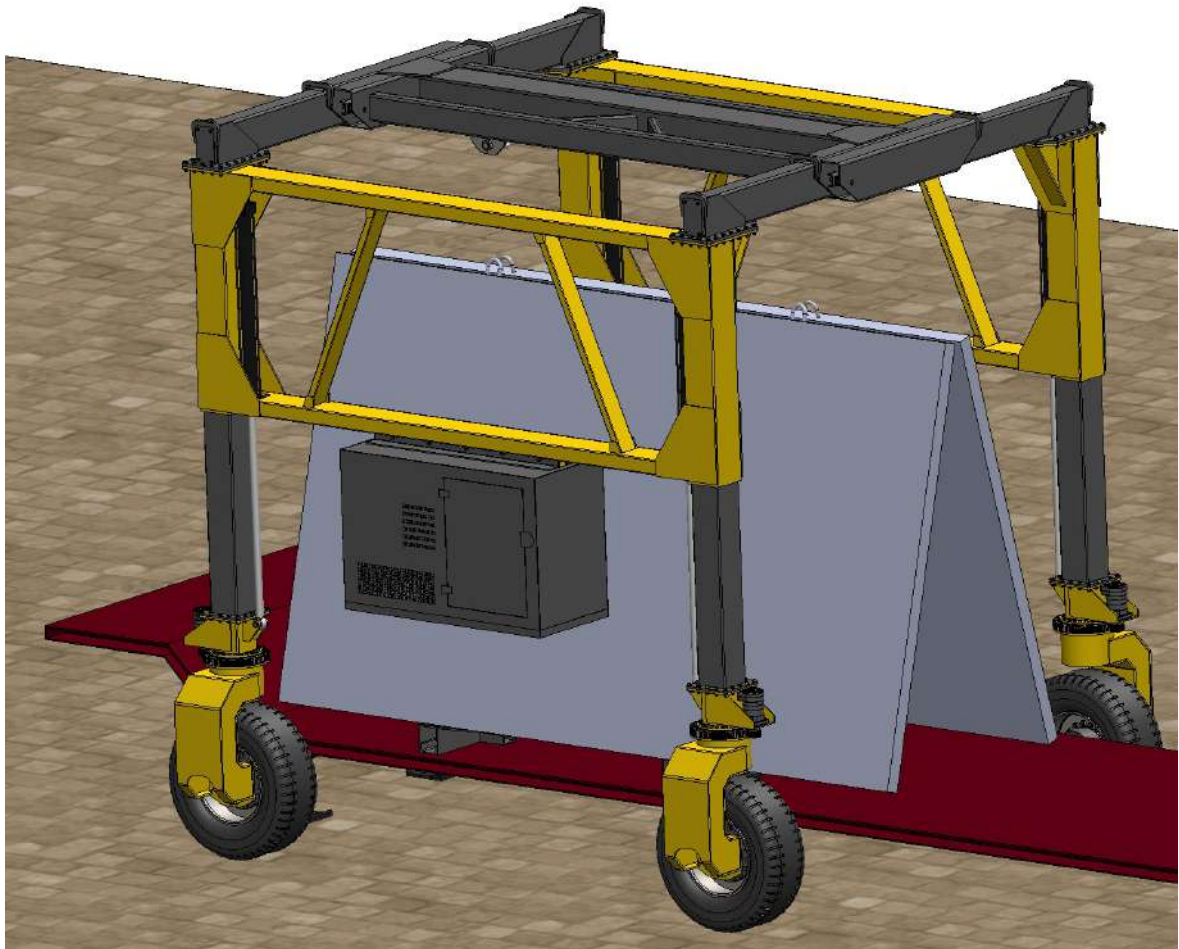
Pórtico móvil posicionado sobre el panel prefabricado de hormigón en el carretón.
